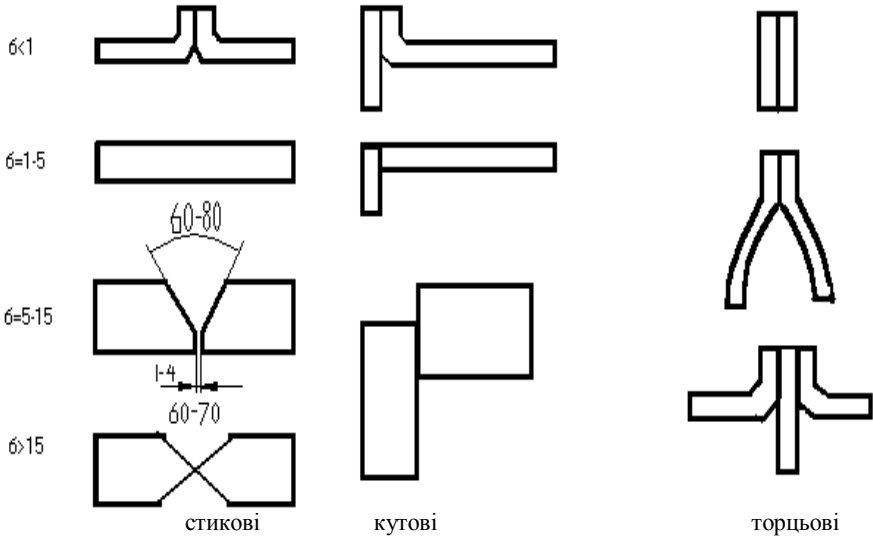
Основні типи зварних з'єднань для газового зварювання
